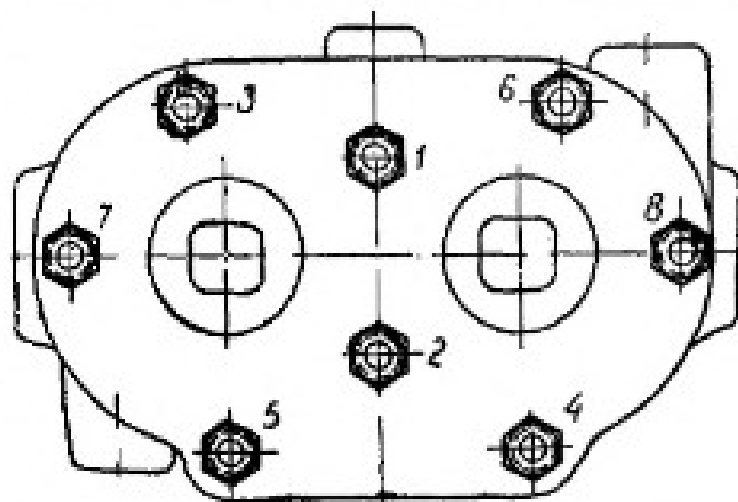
Последовательность затяжки гаек крепления головки цилиндров компрессора.
